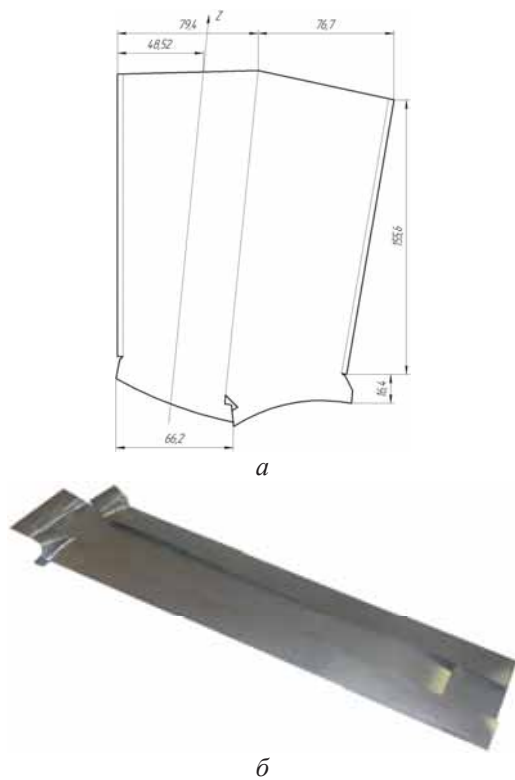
Чертёж кожуха лопатки (а) и отштампованный кожух из титанового листа (б)
